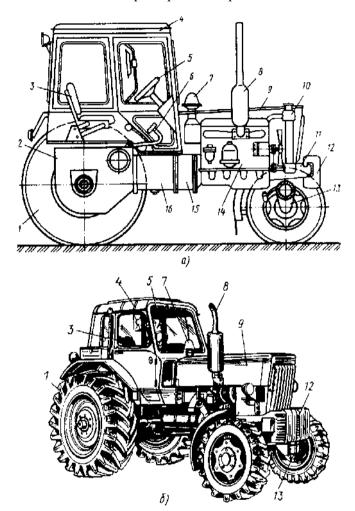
Колесный трактор типа «Беларусь» с передним размещением двигателя: а – компоновка сборочных единиц; б – общий вид; 1 – колесо; 2 – задний мост; 3 – сиденье; 4 – кабина; 5 – рулевое управление; 6 – органы управления; 7 – воздухозаборник; 8 – выхлопная труба; 9 – капот; 10 – радиатор; 11 – подрамник; 12 – контргруз; 13 – передний мост; 14 – двигатель; 15 – муфта сцепления; 16 – коробка передач
